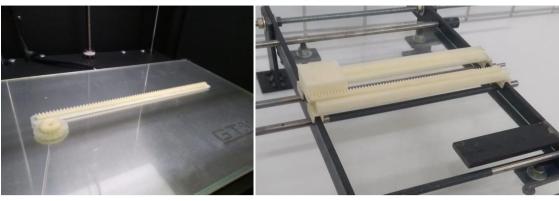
a) Peças sendo impressas; b) peças montada na máquina;
